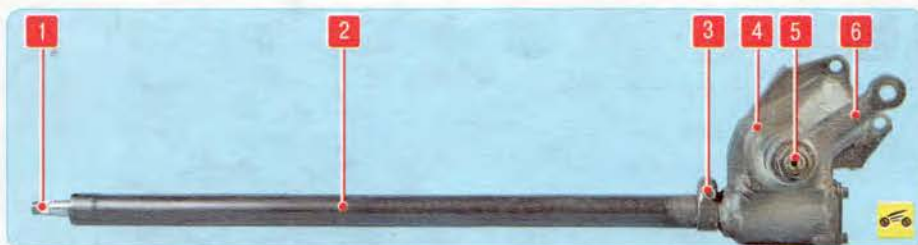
Рулевой механизм: 1 – шлицевое соединение рулевого вала со ступицей рулевого колеса; 2 – корпус рулевого вала; 3 – стяжной болт крепления корпуса рулевого вала; 4 – рулевой механизм; 5 – гайка крепления рычага рулевого механизма; 6 – рычаг рулевого механизма
